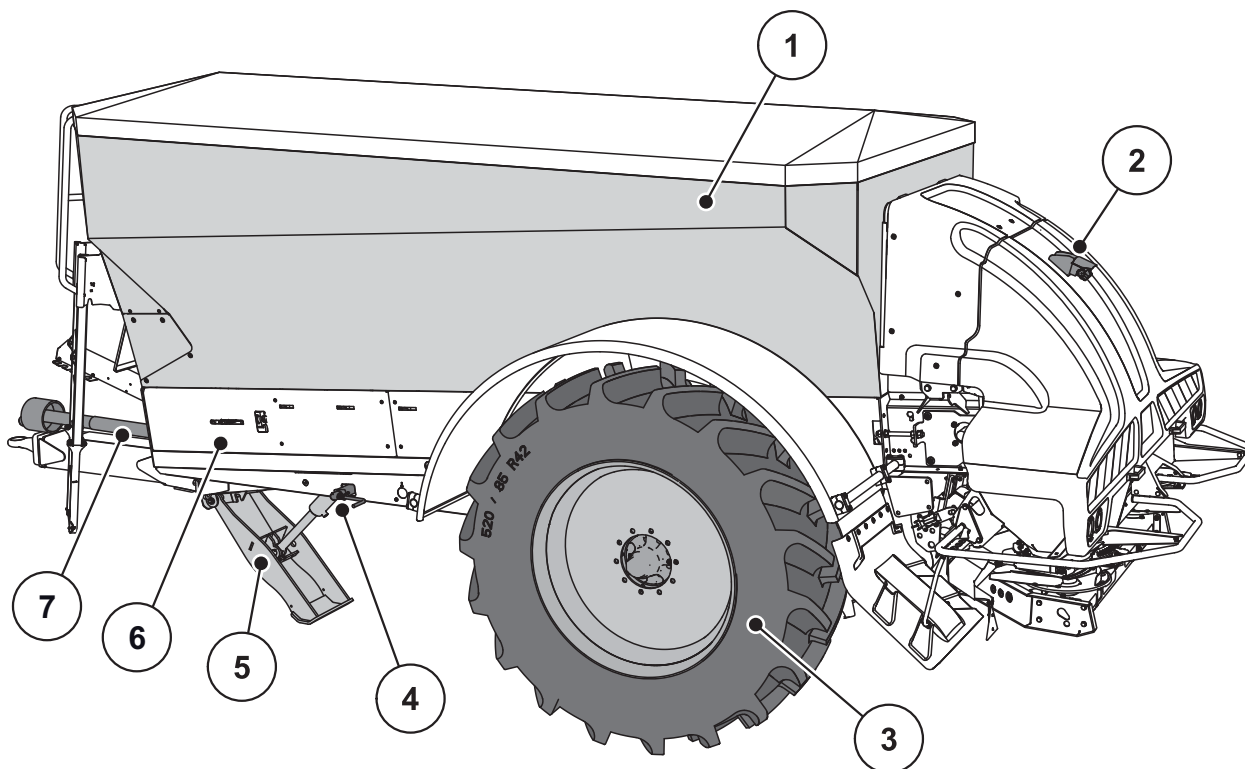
Composants et fonctionnement de la machine AXENT, vue latérale
